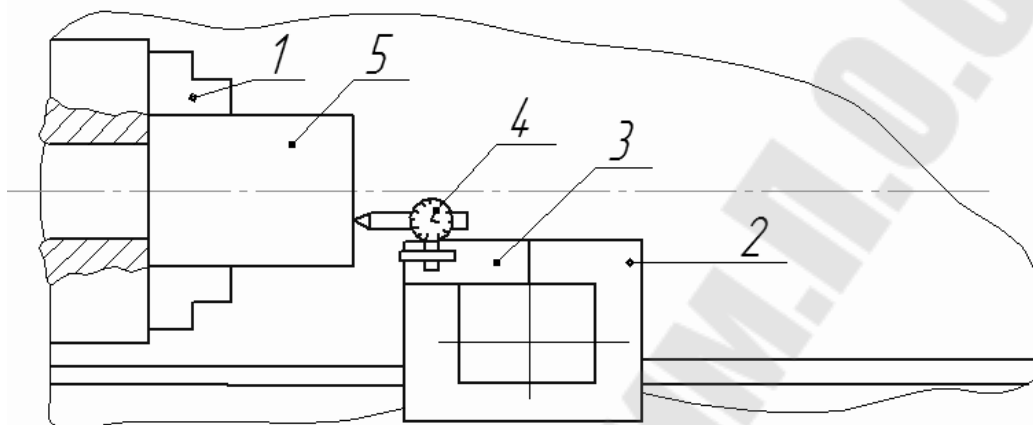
Схема измерения погрешности закрепления заготовки: 1 – трёхкулачковый патрон, 2 – суппорт станка, 3 – штатив с магнитным основанием, 4 – индикатор, 5 – заготовка
